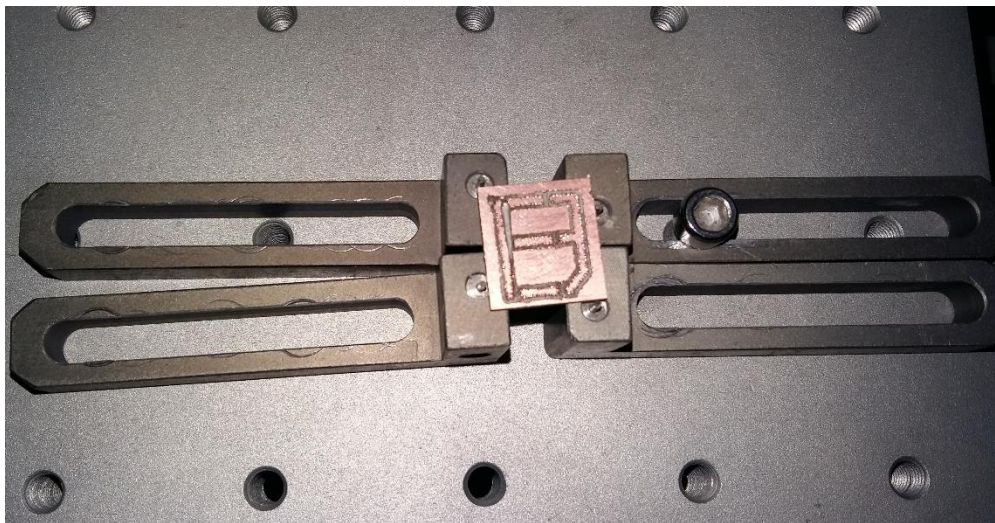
Ubicación de la PCB en la maquina Pick and Place TP220.
